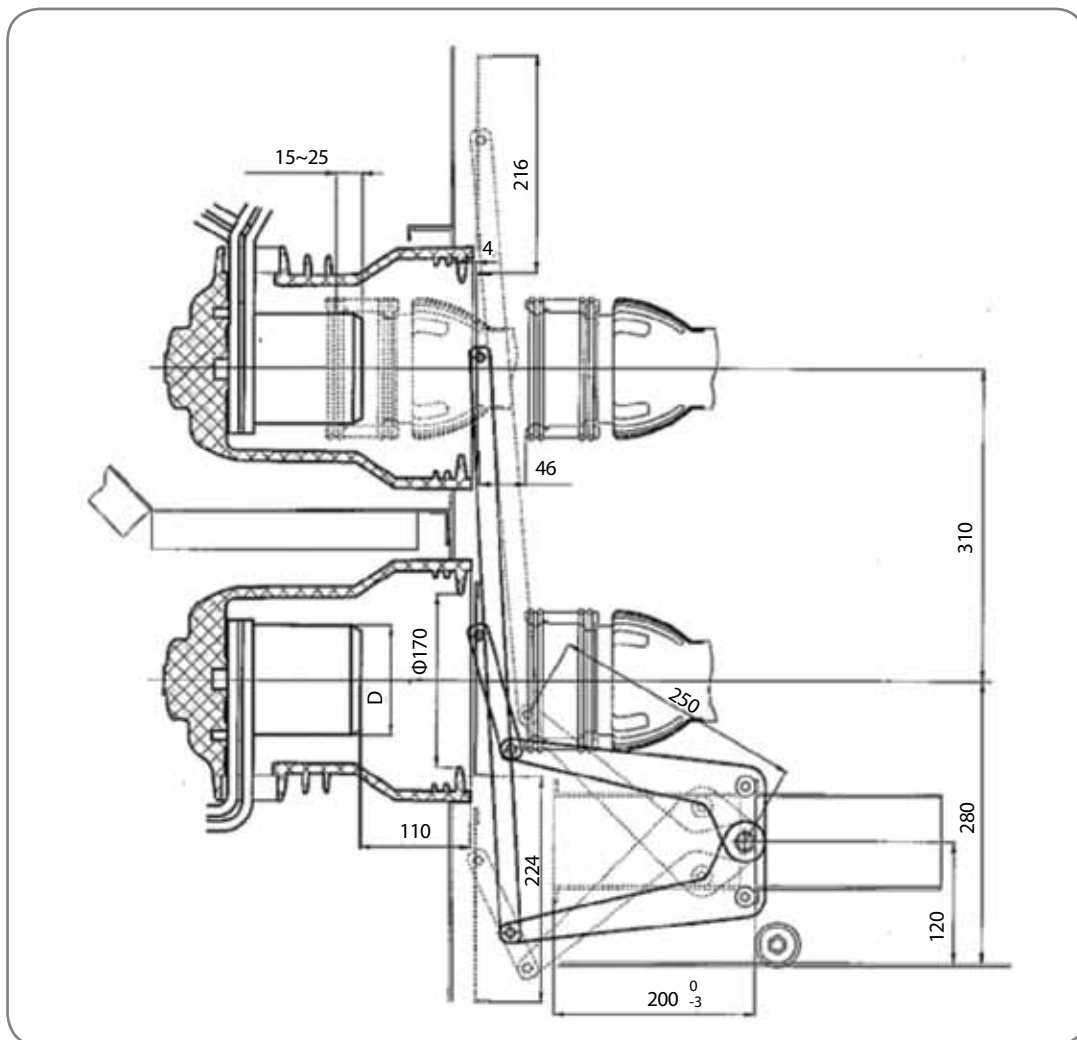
Установочные размеры выключателя HVX-E в ячейке
